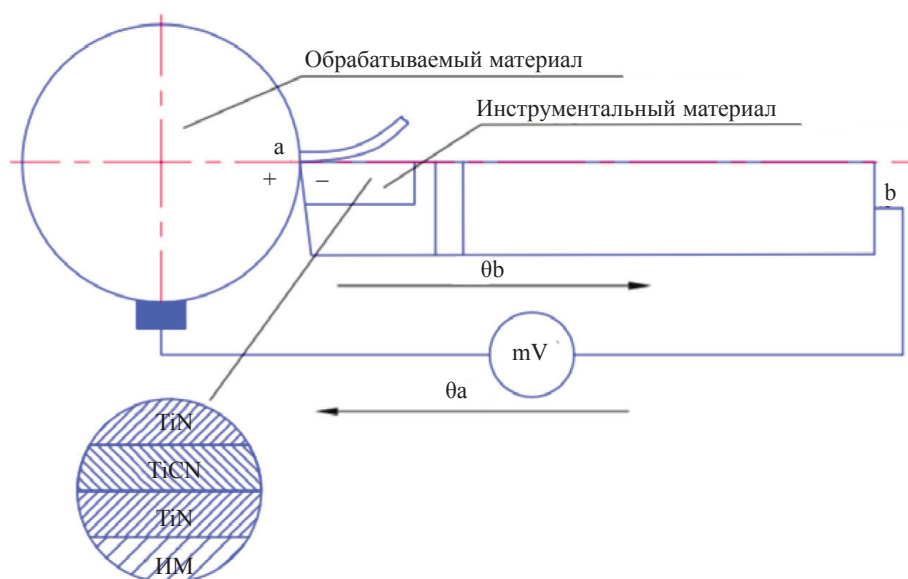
Электрическая цепь естественной термопары режущий инструмент—заготовка [34].
